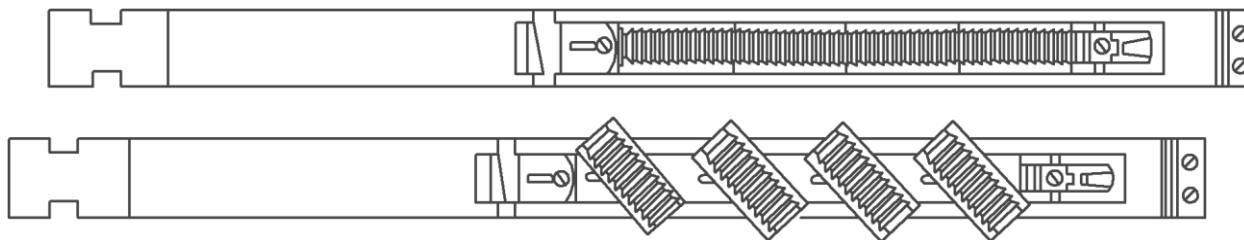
Зовнішня збірна протяжка з хвостовою частиною для роботи на горизонтально-протяжних верстатах
